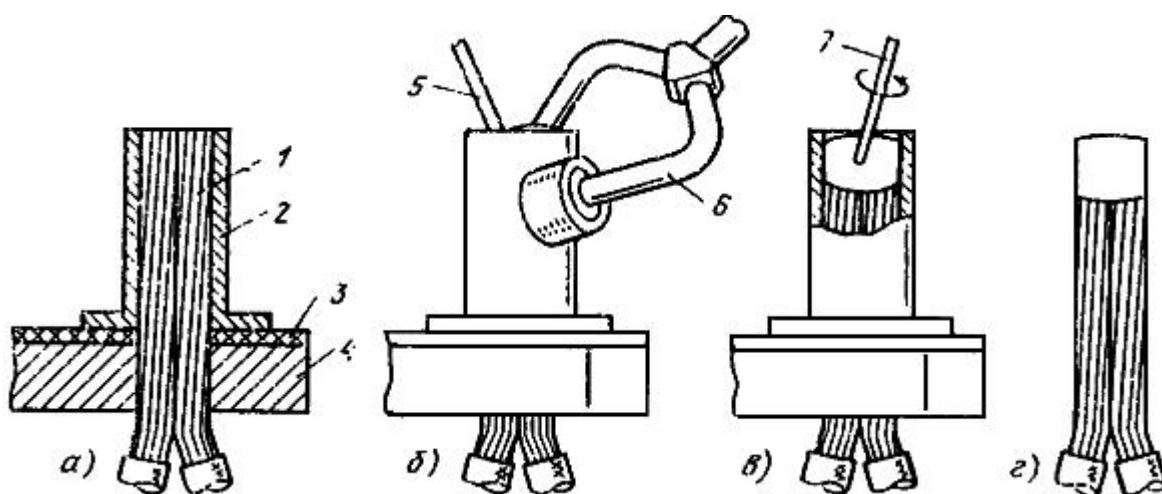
Пропано-кислородная сварка жил сплавлением по торцам
